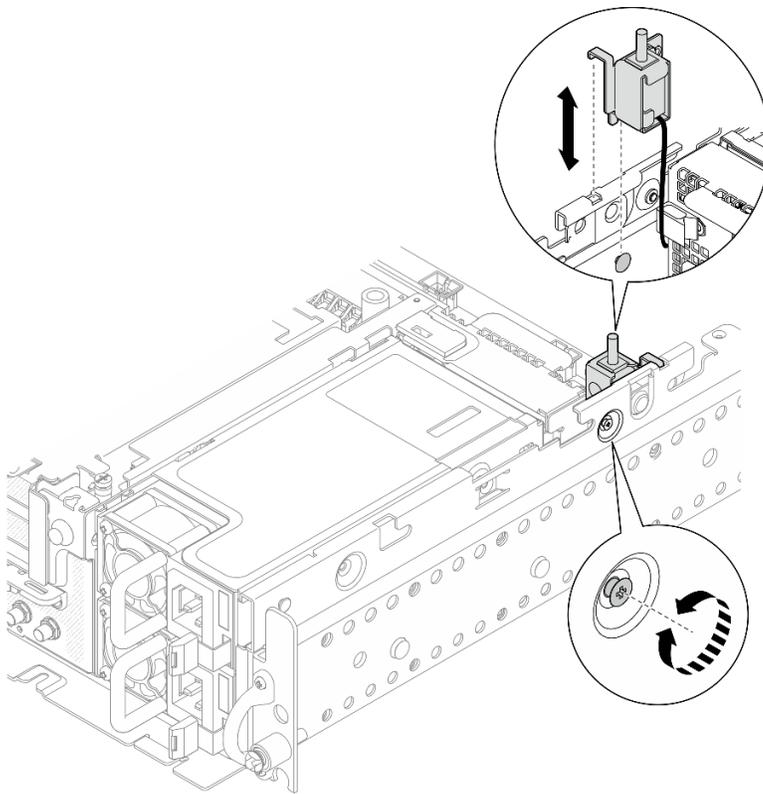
Installieren des Schalters gegen unbefugten Zugriff mit Kabel
